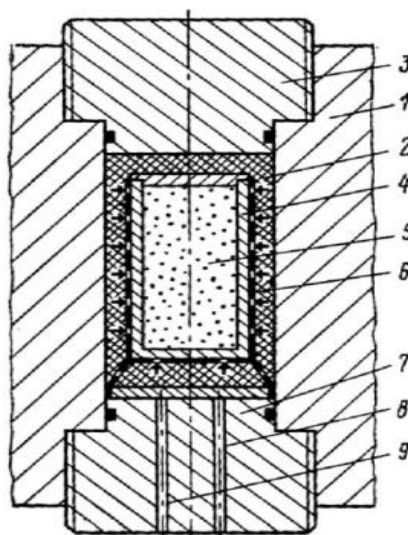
Принципиальная схема изостатического прессования: 1 – сосуд высокого давления; 2 – жидкость высокого давления; 3 – верхний затвор; 4 – упругая форма; 5 – прессуемый порошок; 6 – перфорированная корзина; 7 – нижний затвор; 8 – подвод высокого давления; 9 – отвод жидкости
